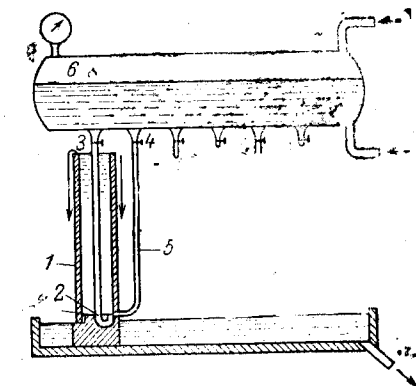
Приспособление для установки стволов в свинцовой ванне.
